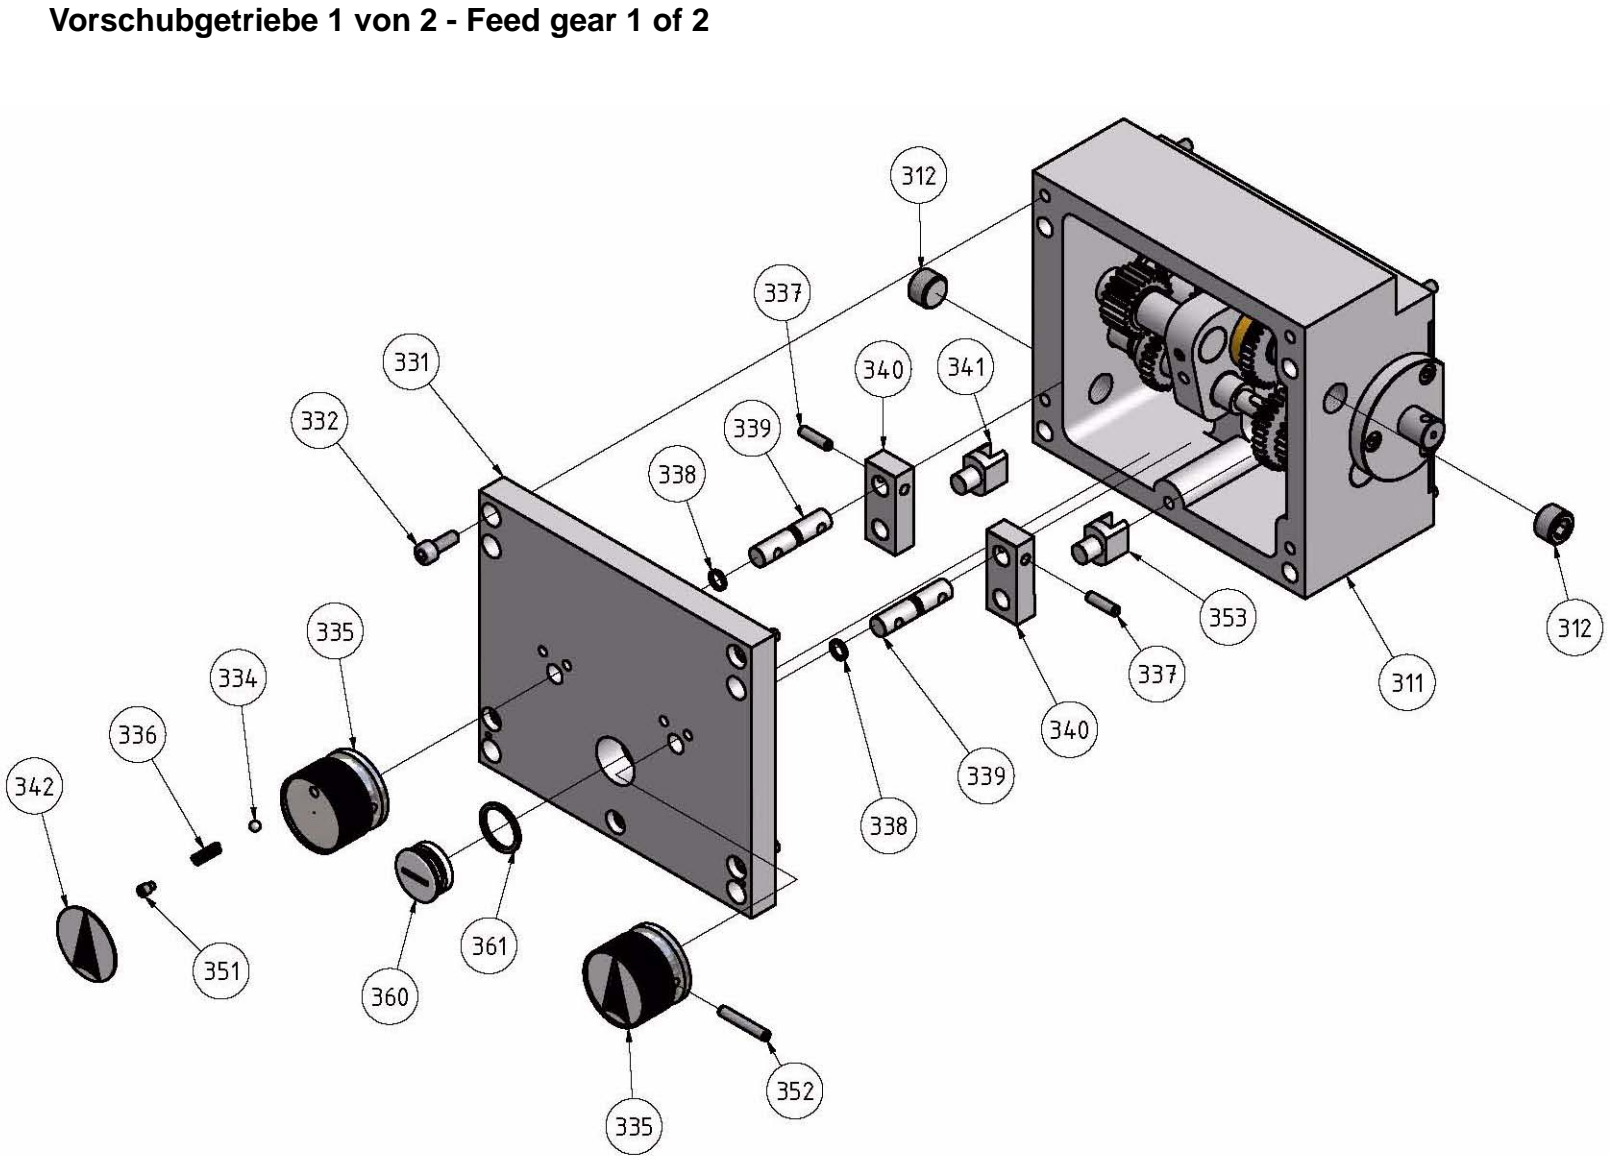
Vorschubgetriebe D280 1 von 2 - Feed gear D280 1 of 2
